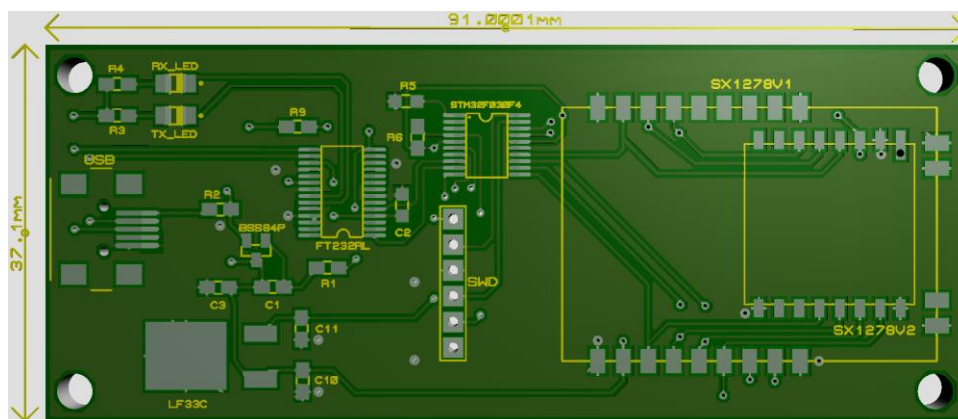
Dimensiones de la PCB para la estación receptora.
